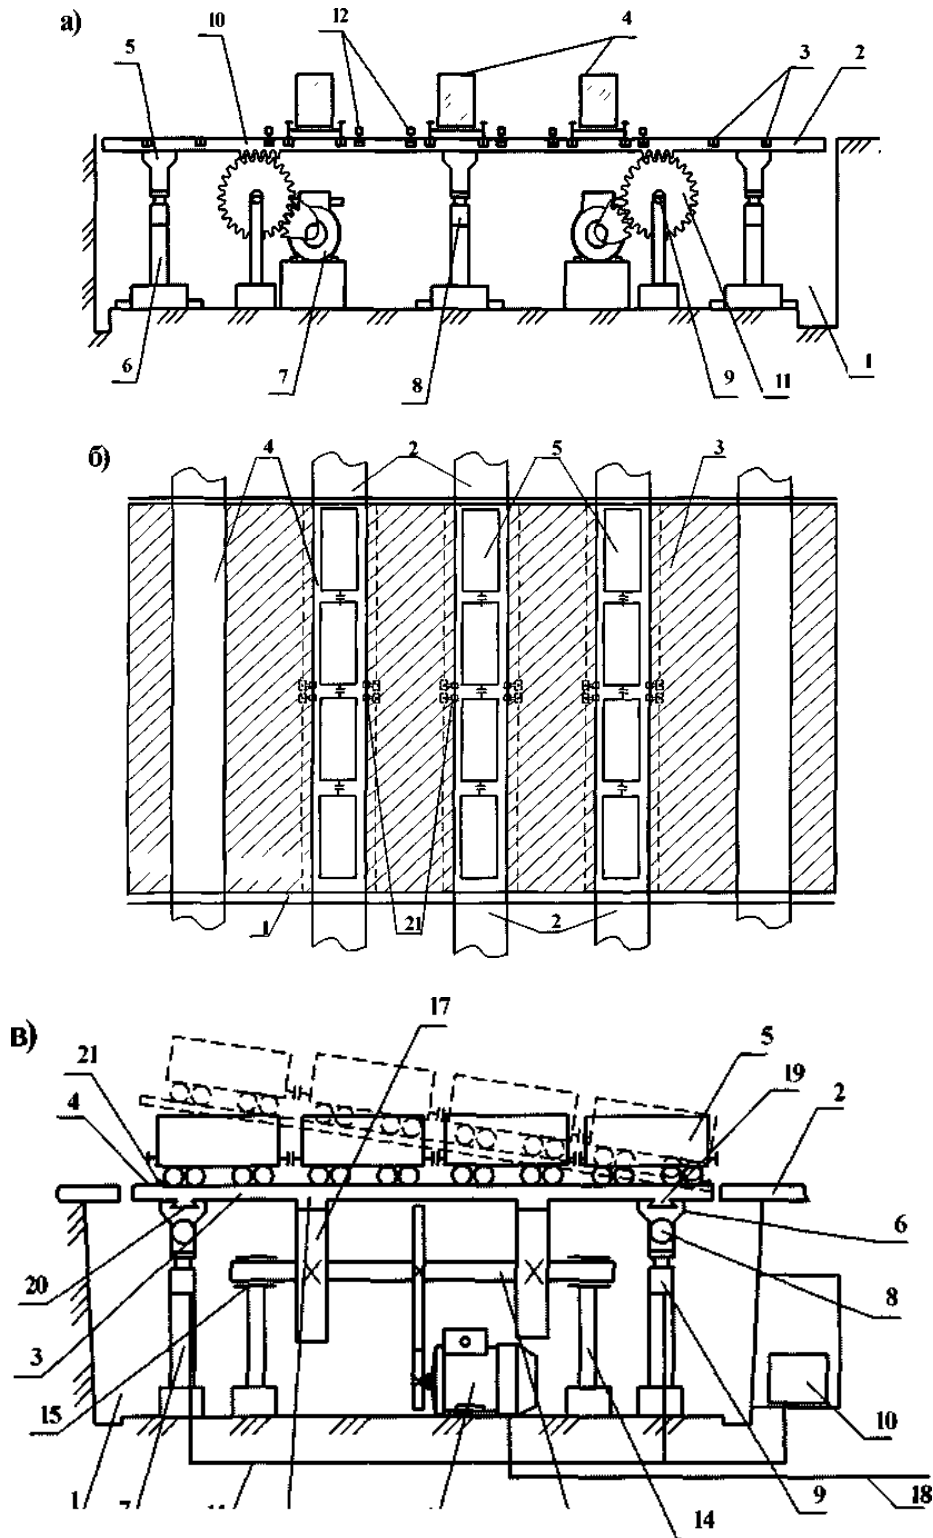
Пристрій для переміщення рейкового транспортного засобу з одного рейкового шляху на паралельний йому шлях: а) вид попереду; б) вид зверху; в) вид збоку
